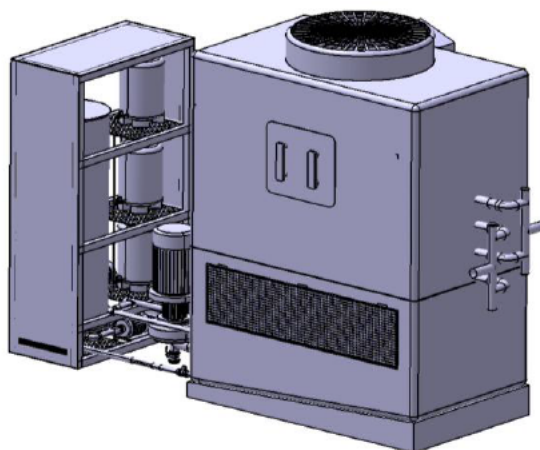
Prototipo desarrollado de enfriador evaporativo higiénico y automático.
